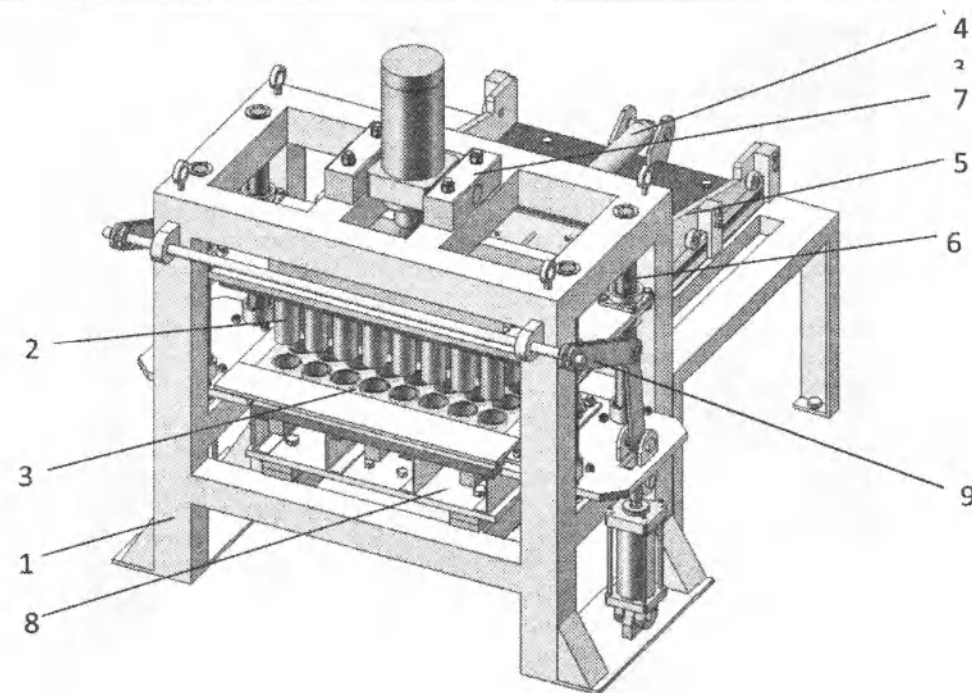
Общий вид брикетного вибропресса: 1 – рама; 2 – пуансон; 3 – матрица; 4 – гидроцилиндр; 5 – приемно-загрузочное устройство; 6 – направляющие; 7 – траверса; 8 – стол и площадка вибратора; 9 – шарнирный рычаг синхронизации цилиндров матрицы.
